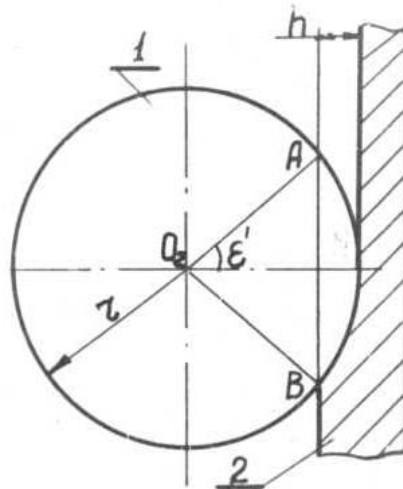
Схема установки расточного круглого резца относительно стенки цилиндра. 1 – резец; 2-цилиндр
